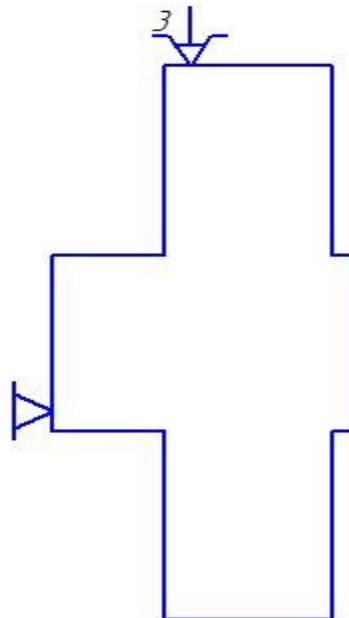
Схема базування в трьохкулачковому патроні із механічним затисканням з упором в торець.
